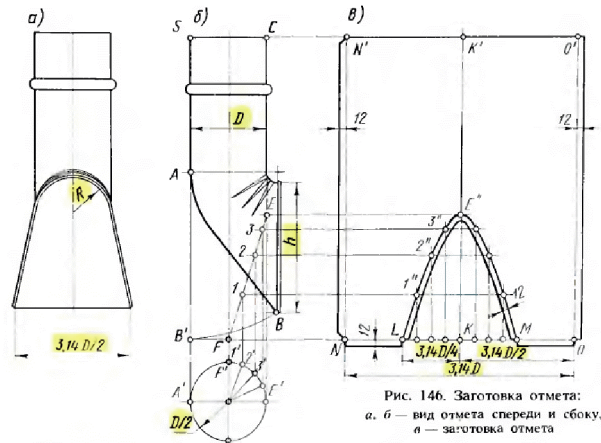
Заготовка отмета: а, б — вид отмета спереди и сбоку, в — заготовка отмета
